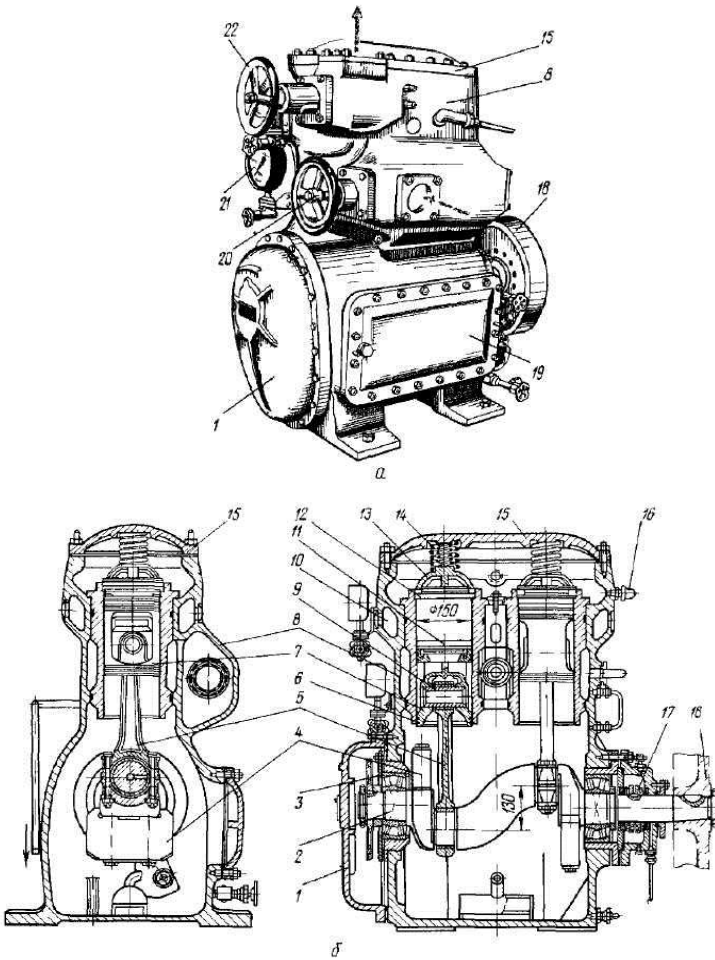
Блок-картерний компресор АВ-100: 1 – кришка картера; 2 – колінвал; 3 – корінні підшипники; 4 – противаги; 5 – шатуни; 6 – мастилознімальні кільця; 7 – поршень; 8 – блок-картер; 9 – палець; 10 – водяна сорочка; 11 – клапан усмоктувальний; 12 – нагнітальний клапан; 13 – притискна склянка; 14, 15 – буферні пружини; 16 – клапан запобіжний; 17 – сальник; 18 – маховик; 19 – бічна кришка; 20 – запірний всмоктувальний клапан; 21 – манометр; 22 – нагнітальний вентиль
